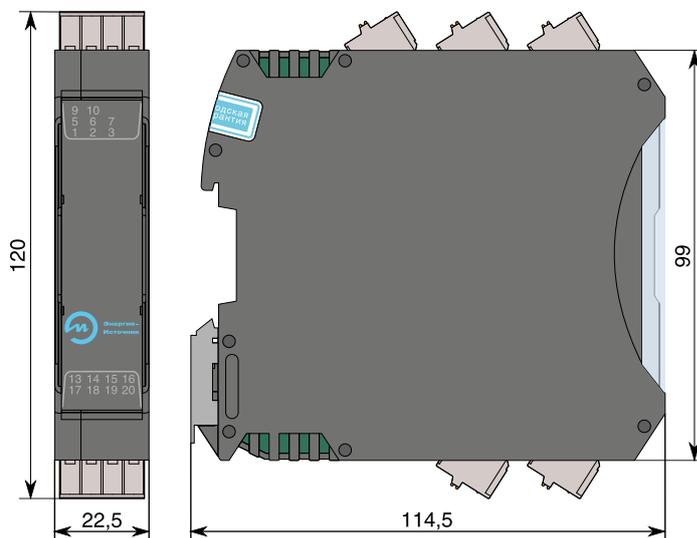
Габаритные размеры модуля в корпусе шириной 22,5 мм с разъемами с пружинными клеммниками и тестовыми гнездами
